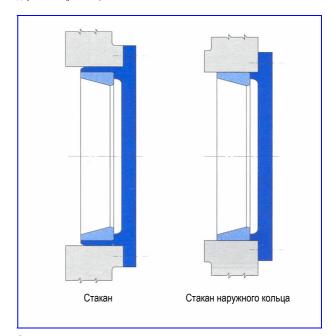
Приспособления для установки подшипников - О-сопряжение.
